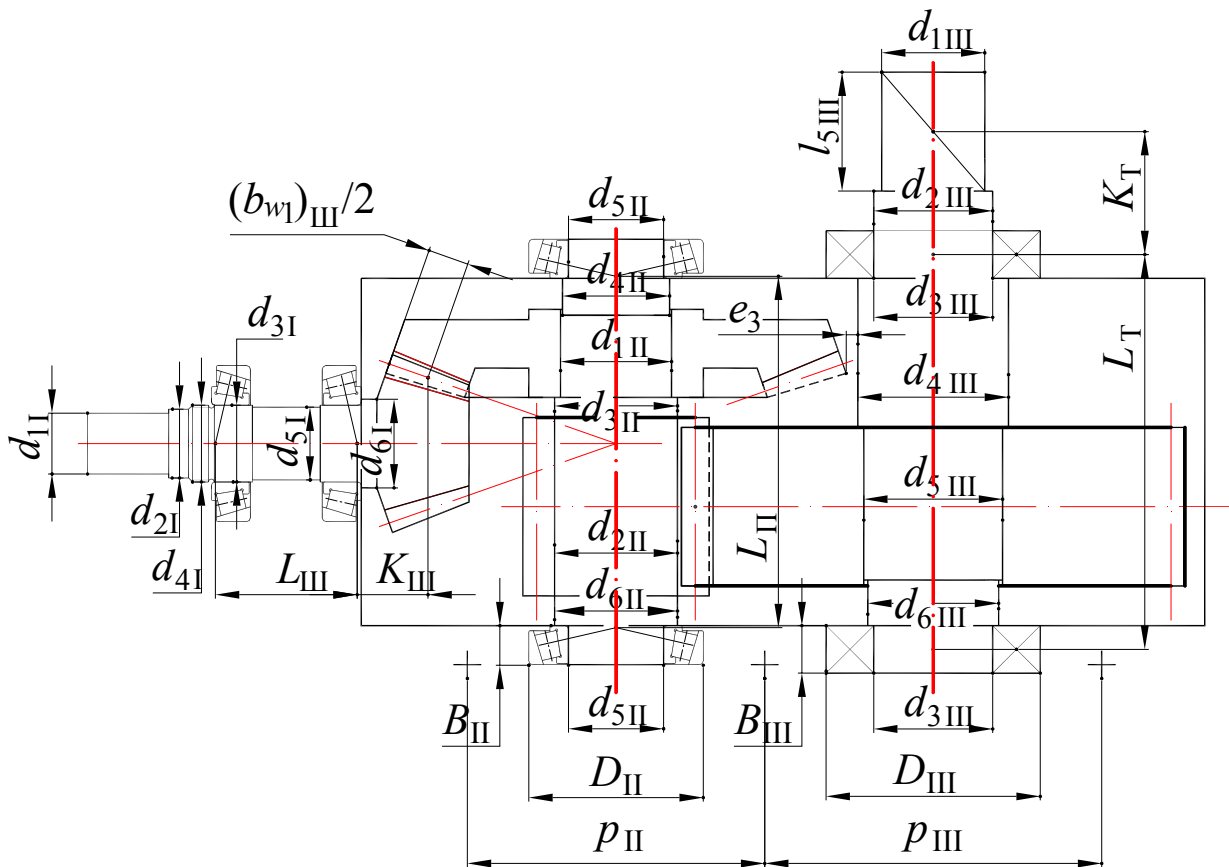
Остаточний результат ескізного компоунання редуктора за умови встановлення підшипників вала I «у розтяжку»
